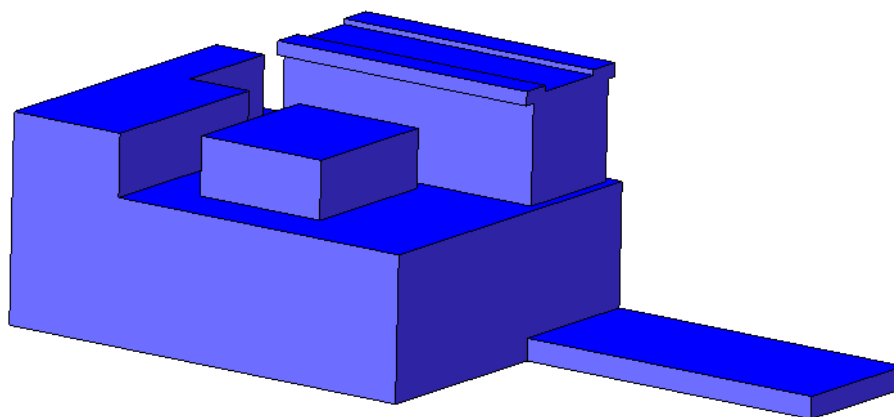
Станина оброблювального центра IPT180ПМФ4
